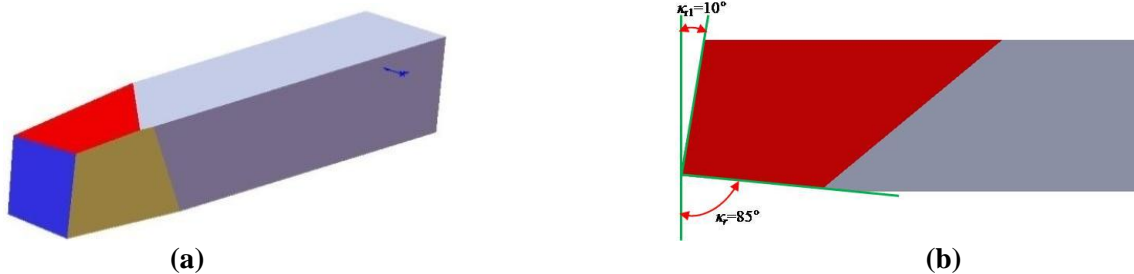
Géométrie d'outil de tournage pour $\kappa_r = 85^\circ$.
